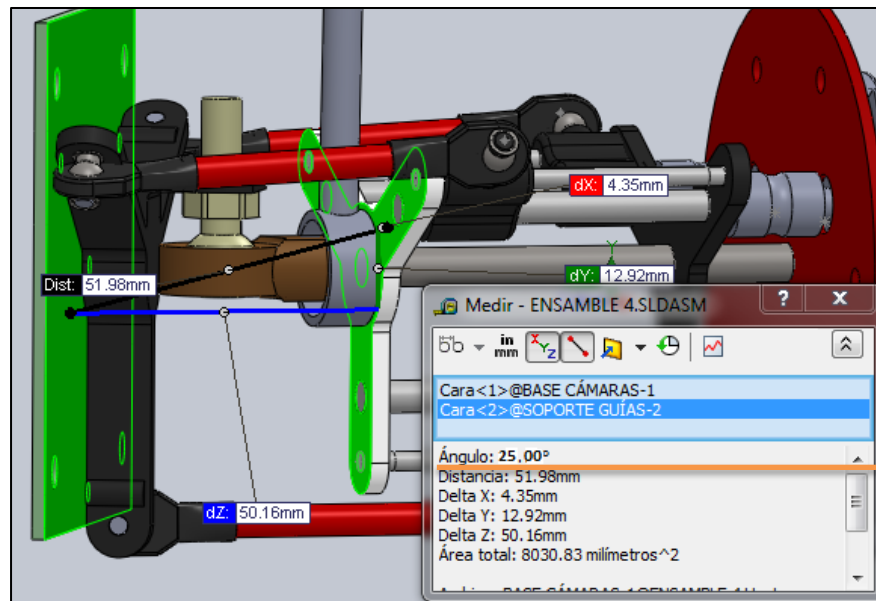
Angulo de rotación de la placa frontal con carrera de 47 mm
